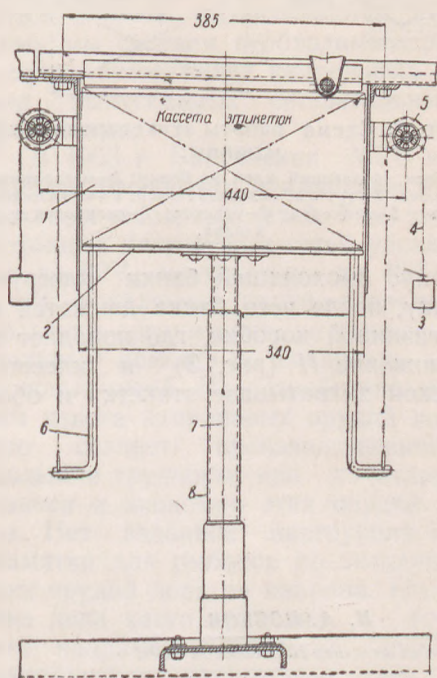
Механизм для подачи этикеток: 1—магазинная коробка; 2—планка; 3—грузик; 4—гибкий тросик; 5—ролики; 6—крючкообразный рычаг; 7—шток; 8—направляющая втулка.
